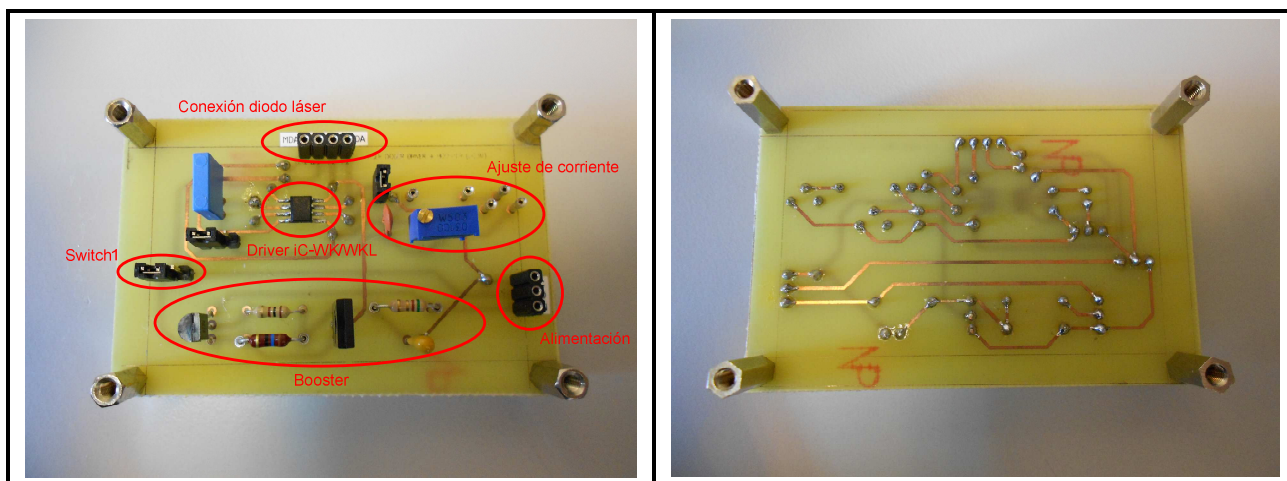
Imagen de las dos caras de la PCB con booster. Top [Izda.] y Bottom [Dcha.].
